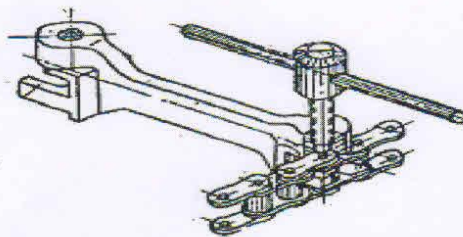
Приспособление для разборки втулочно-роликовых цепей
